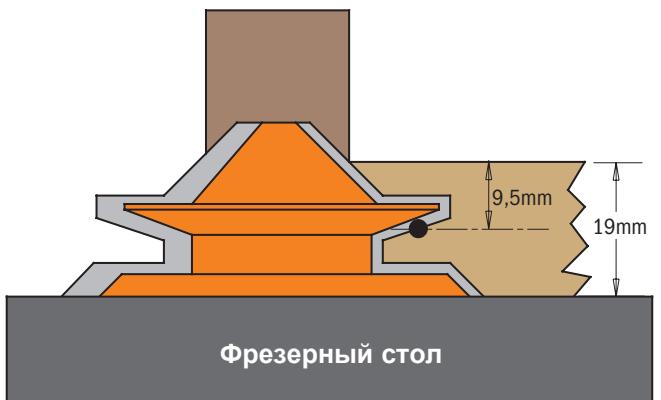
Отфрезеруйте первую деталь внутренней стороной вниз. Убедитесь, что рез проходит через центр детали как на рисунке.
